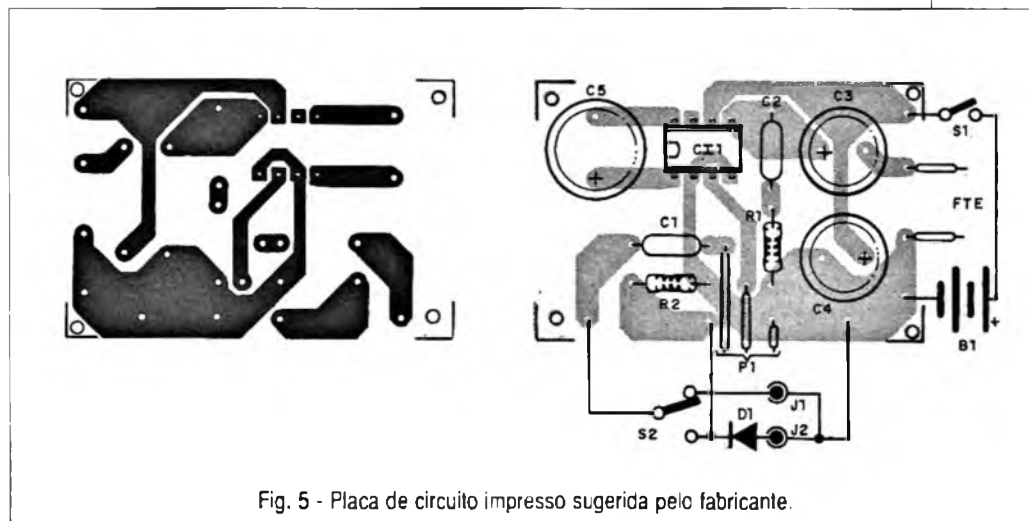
Placa de circuito impresso sugerida pelo fabricante.
